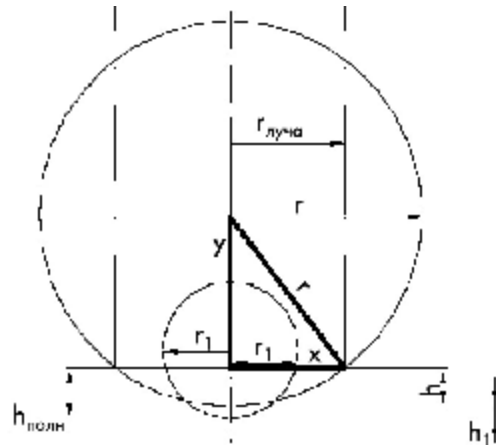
Схема расчета угла наклона стыковой плоскости при сварке разнородных металлов
